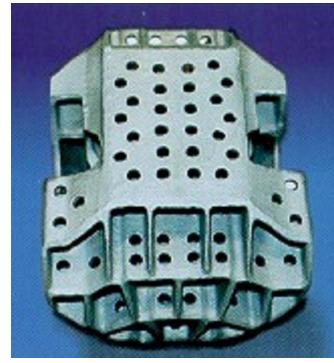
Відливка деталі внутрішнього привода клапана з нержавіючої сталі
